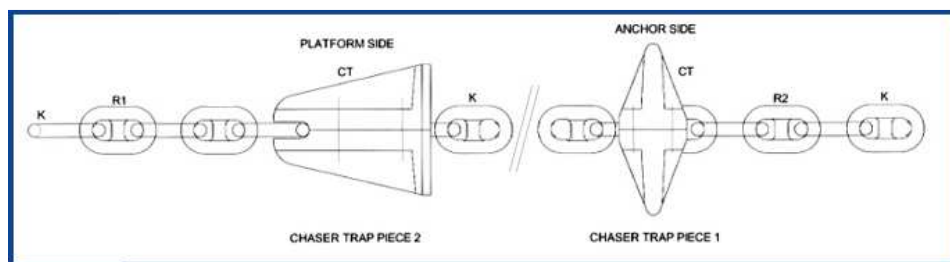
Chaser Trap. Fonte: (Chaser Trap)
